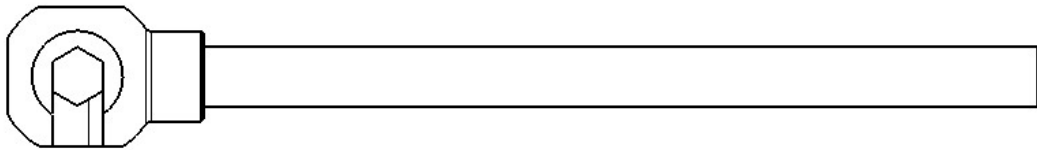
D: Notfallwerkzeug für stecken gebliebenen Bohrstahl 9 307 01 036
